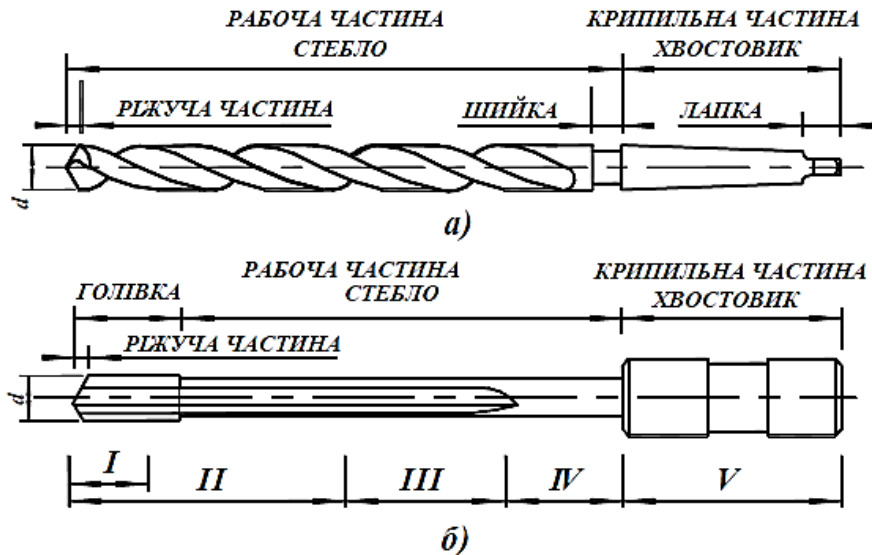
Конструктивні елементи різноманітних ріжучих інструментів для свердлування: а) спіральне або гвинтове свердло; б) свердло одностороннього різання. d – діаметр свердла; I – запас на переточку; II – глибина свердлування; III – довженна корпусу кондуктора с кондукторною втулкою; IV – довженна люнета (люнетів) для підтримання и направлення свердла; V – довженна хвостовика.
